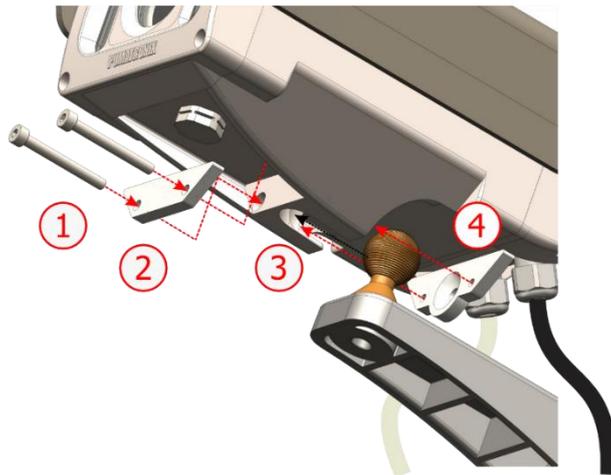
Montagem do Fixador da VIGIA+: 1) Parafusos M4 Allen 3mm (2 unidades); 2) Reforço; 3) Cavidade da VIGIA+; 4) Fixador
